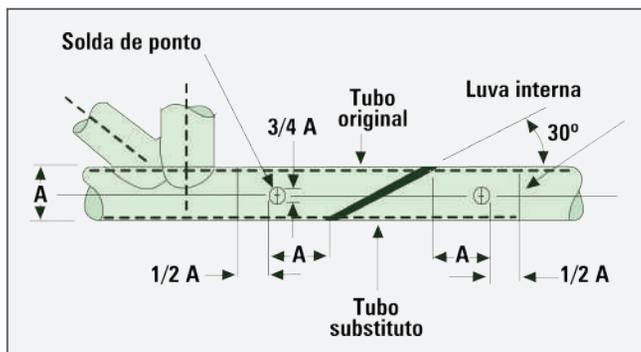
Posicionamento e dimensões do reparo com luva interna
